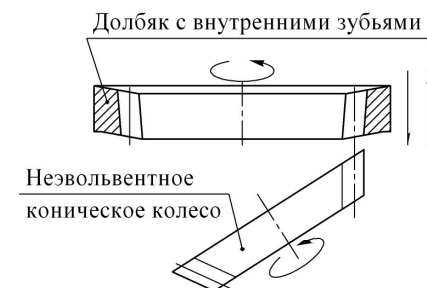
Схема формирования зубьев конической шестерни долбяком с внутренними зубьями
